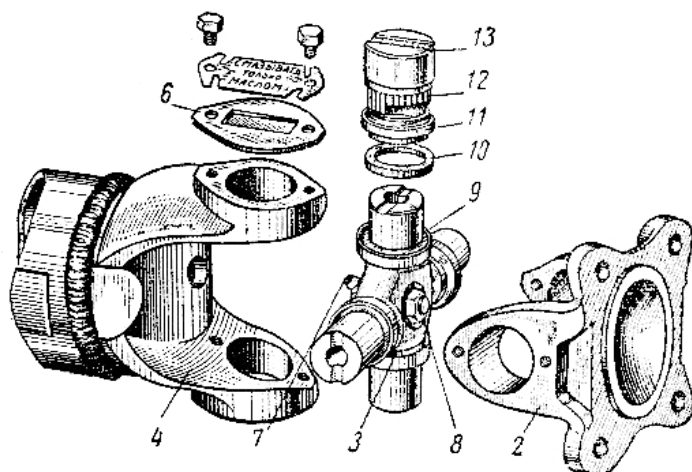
Жесткий карданный шарнир неравных угловых скоростей: 2, 4 — вилки; 3 — крестовина; 6 — крышка подшипника; 7, 8 — масленка с клапаном; 9, 10 — уплотнение, 11, 12, 13 — подшипник
